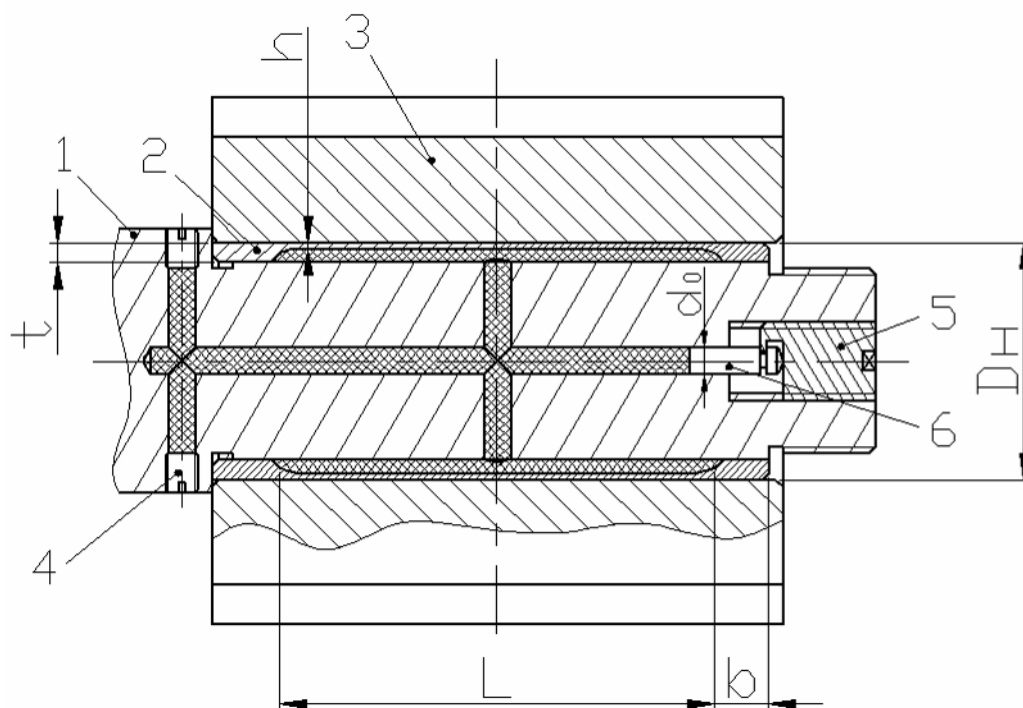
Схема установки фрезы за счет самоцентрирующей втулки
